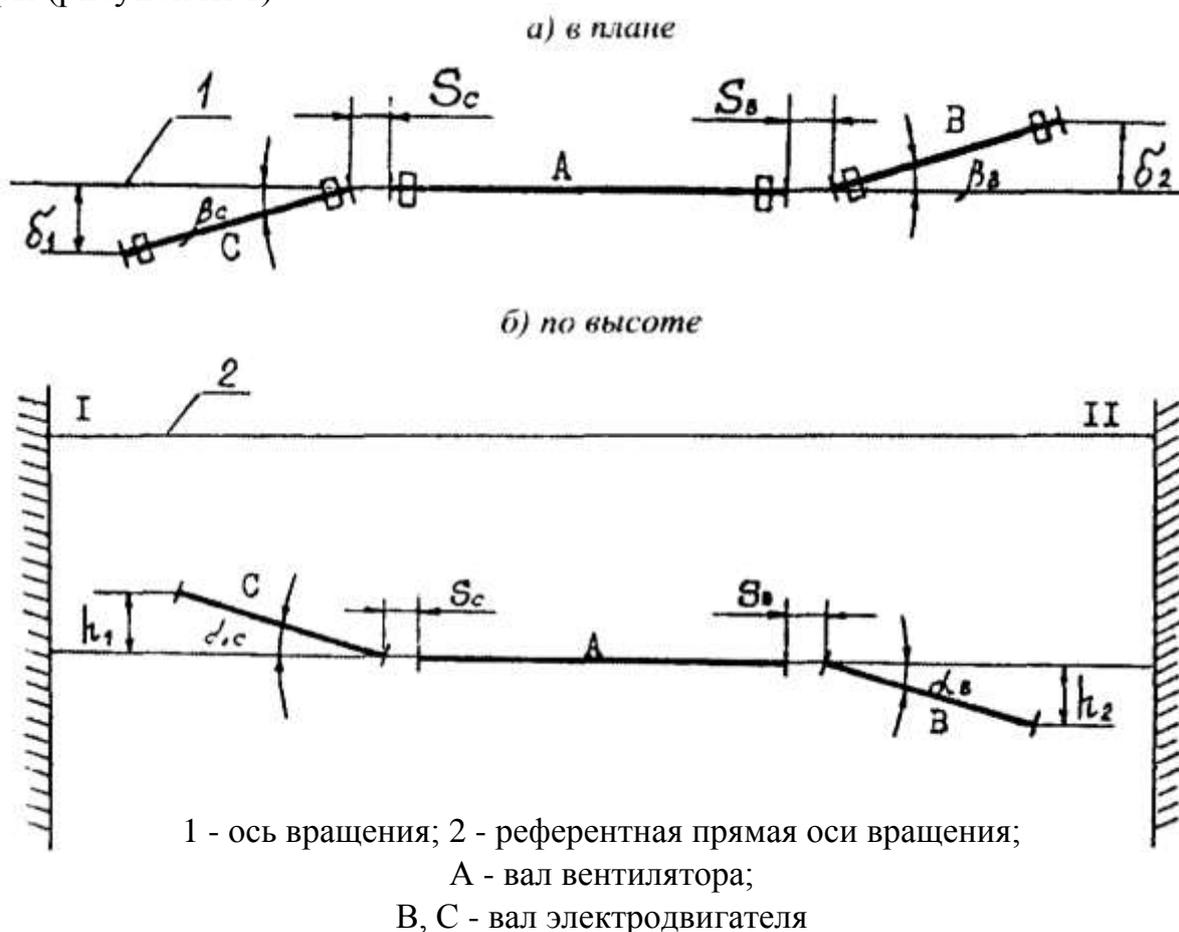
Схема проверки вентиляторной установки ВЦД - 47У
